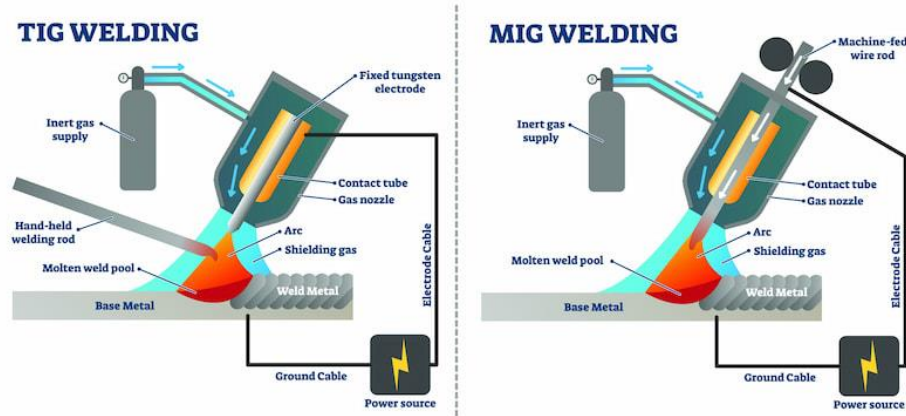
Diferencias entre la soldadura TIG y MIG
